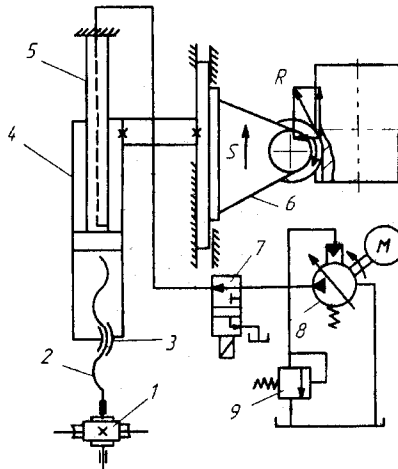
Усування зазору у парі гвинт-гайка зубофрезерного верстата
